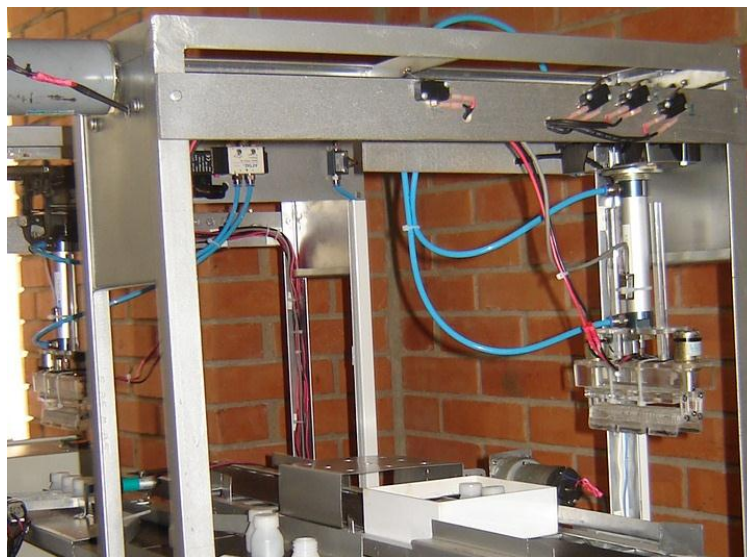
Sensores de Posición en un Puente de la Máquina. [4]
